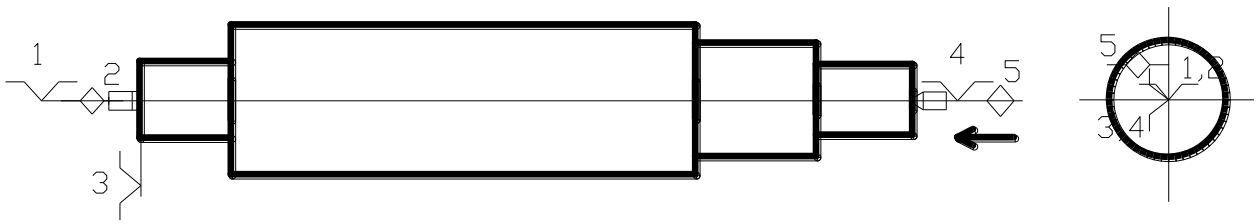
Чистові технологічні бази при обробці поверхонь обертання в центрах
